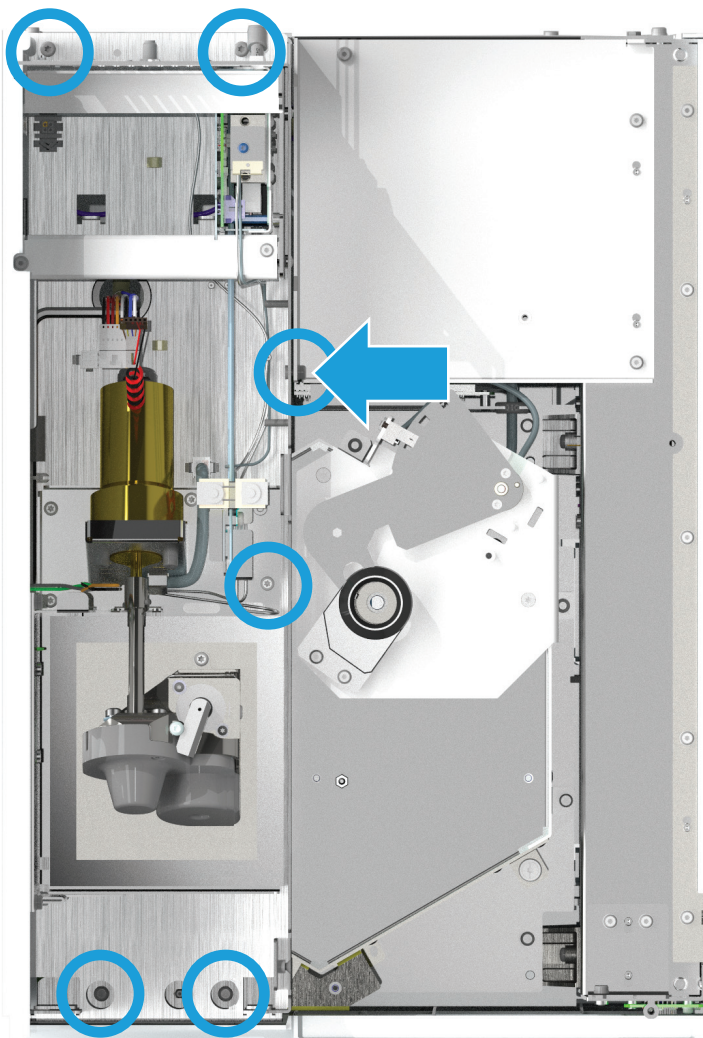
Desserrez les vis qui fixent l'ensemble pneumatique
